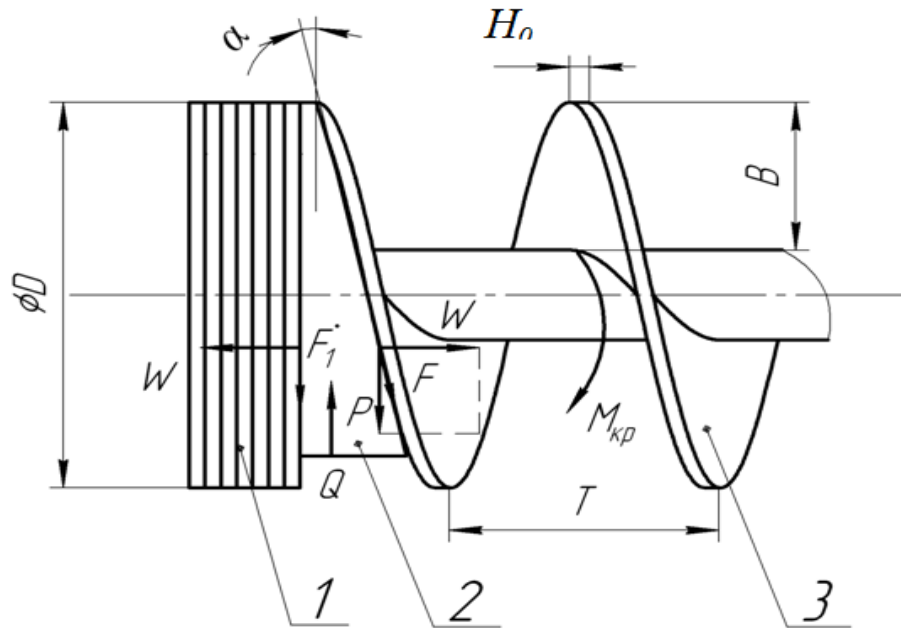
Розрахункова схема пристосування для калібрування витка гвинтової заготовки на крок: 1 – щільно навита заготовка, 2 – клин; 3 – калібровані витки гвинтової заготовки
